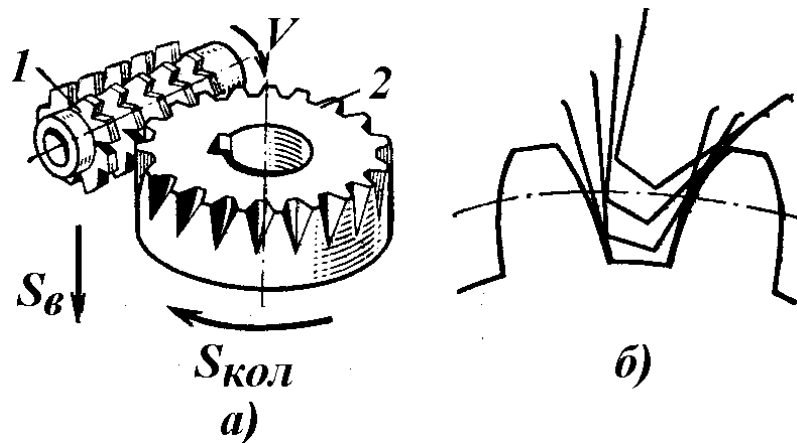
Схема формоутворення зубів циліндричного колеса черв'ячною фрезою: 1 – черв'ячна фреза; 2 – заготовка
